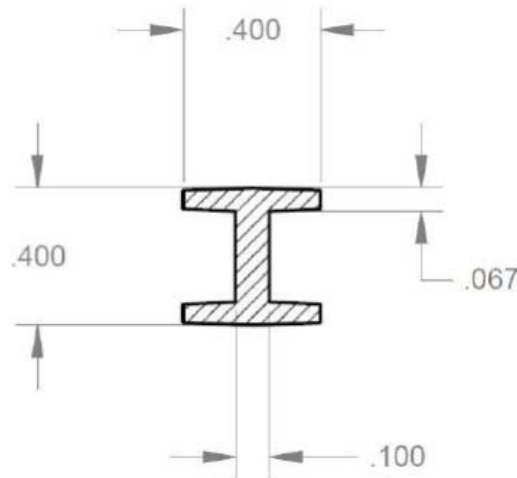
Sección transversal de las vigas I (unidades en pulgadas)
